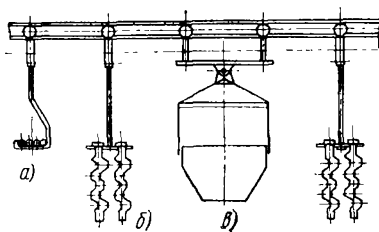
Конструкция подвесок и схема их расположения: а — подвеска, предназначенная для транспортировки мелких поковок в люльках; б — подвеска для поковок средних размеров; в — подвеска для крупногабаритных поковок
